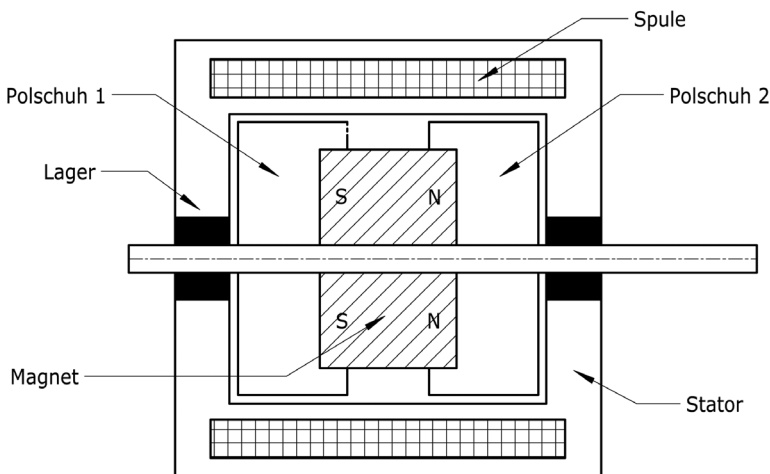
Ein Hybrid-Schrittmotor im Längsschnitt
